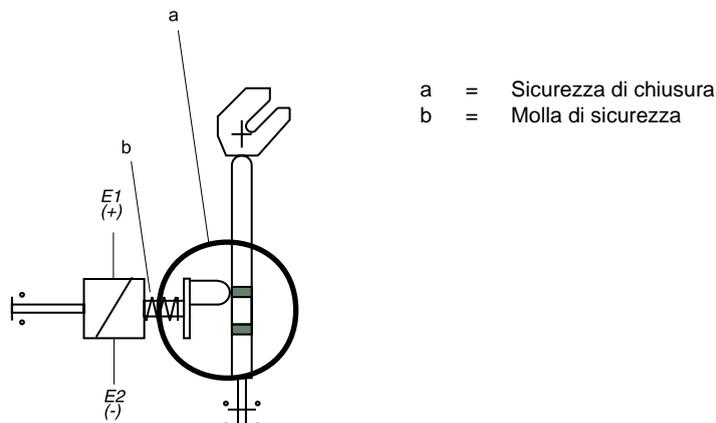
Interruttore bloccaporta di sicurezza con dispositivo di chiusura assicurata integrato
